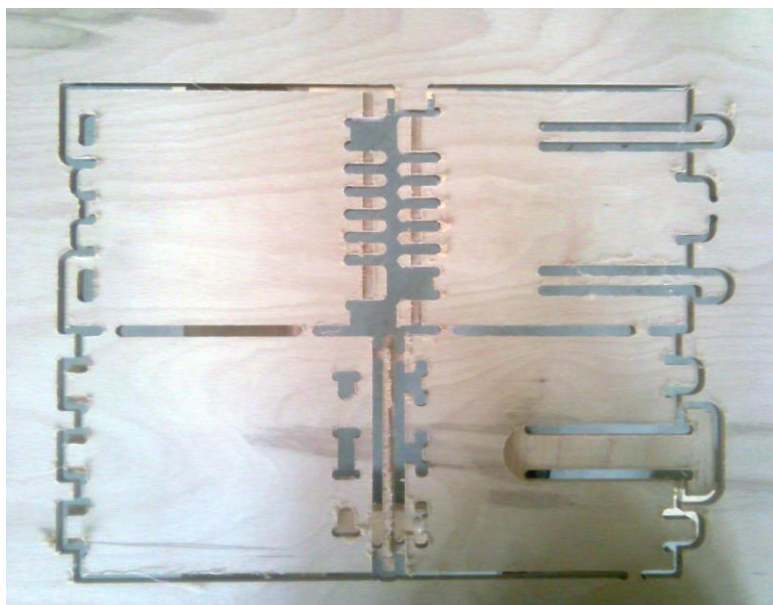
Vizualizace zamýšleného vzorku CNC spojů
